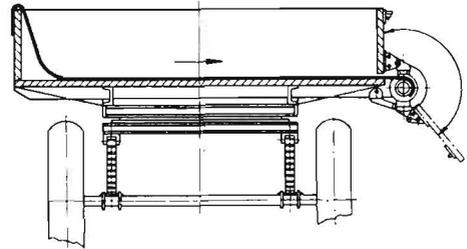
Seitliches Entladen mit Hilfe einer Walze
